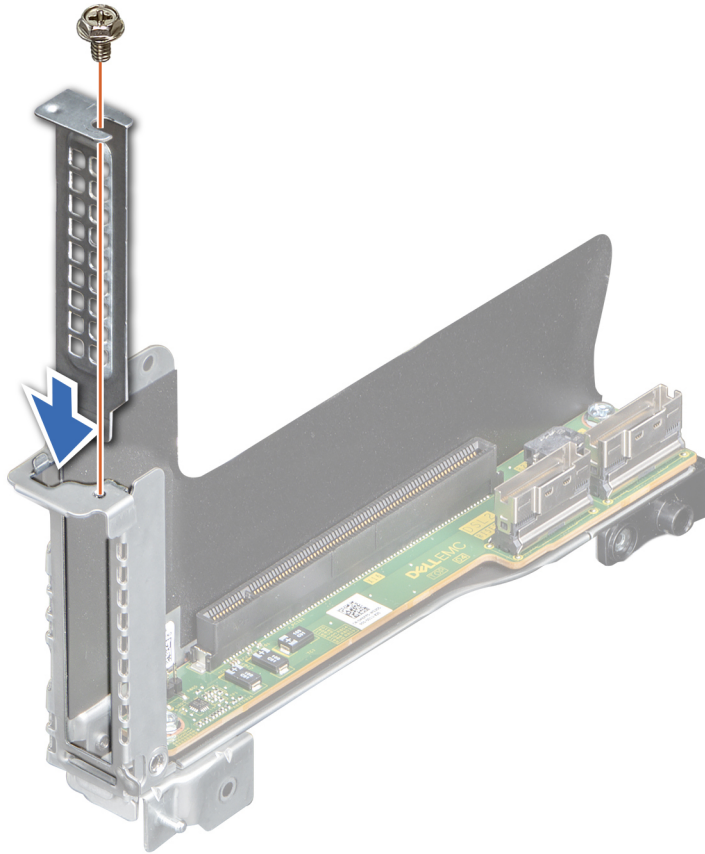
Installation de la plaque de recouvrement de la carte d'extension dans la carte de montage 2
